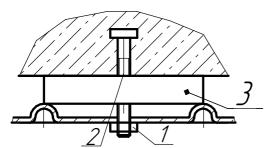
1 - корпус в сборе; 2 - крышка; 3 - рассеиватель.
